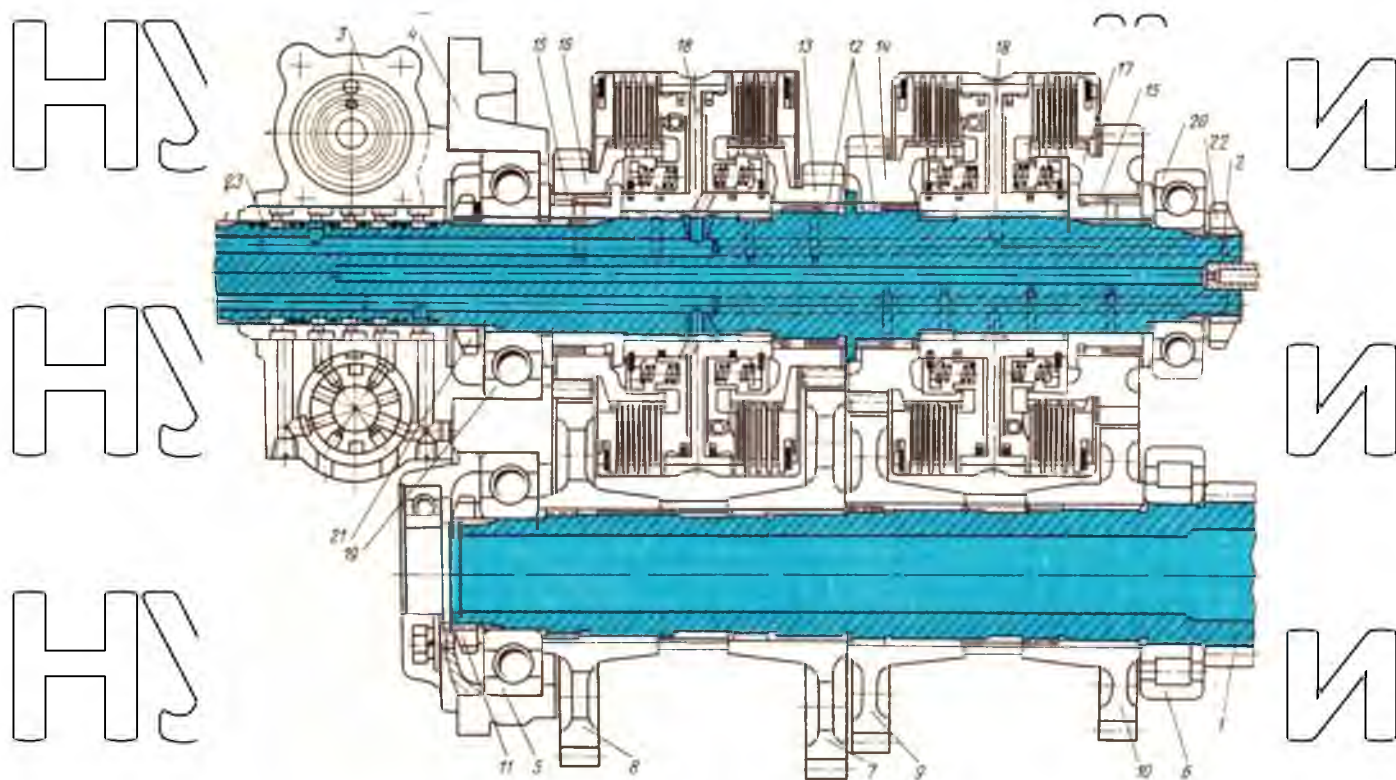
Первинний і проміжний валі в зборі: 1 - проміжний вал; 2 - первинний вал; 3 - розподільник; 4 - стакан; 5, 19 і 20 - підшипники; 6, 12 і 15 - роликові підшипники; 7 - ведена шестерня I передачі; 8 - ведена шестерня II передачі; 9 - ведена шестерня III передачі; 10 - ведена шестерня IV передачі; 11, 21 і 22 -
